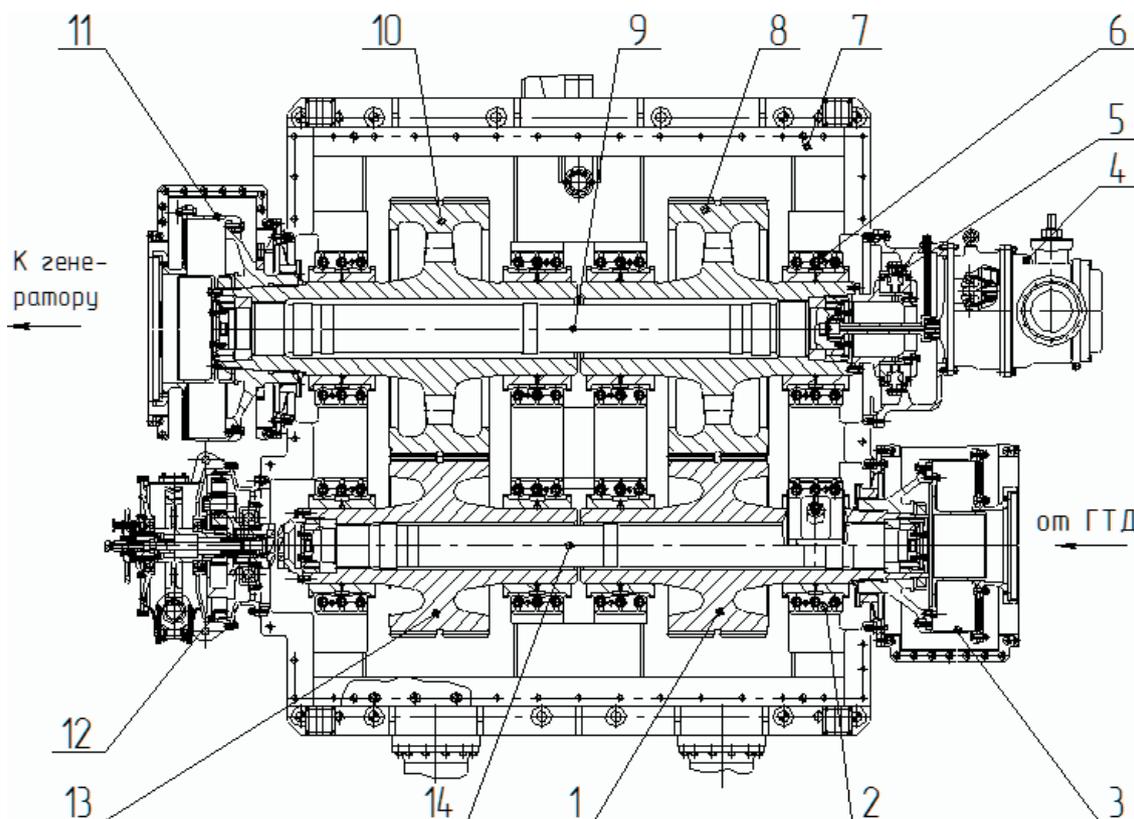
Конструкция редуктора со снятой крышкой: 1,13 – ведущие шестерни; 2,6 – опорные подшипники скольжения; 3,11 – дисковые муфты; 4 – маслоагрегат; 5 – упорный (фиксирующий) подшипник скольжения; 7 – корпус; 8, 10 – ведомые зубчатые колеса; 9,14 – торсионные валы; 12 – электровалоповоротное устройство
